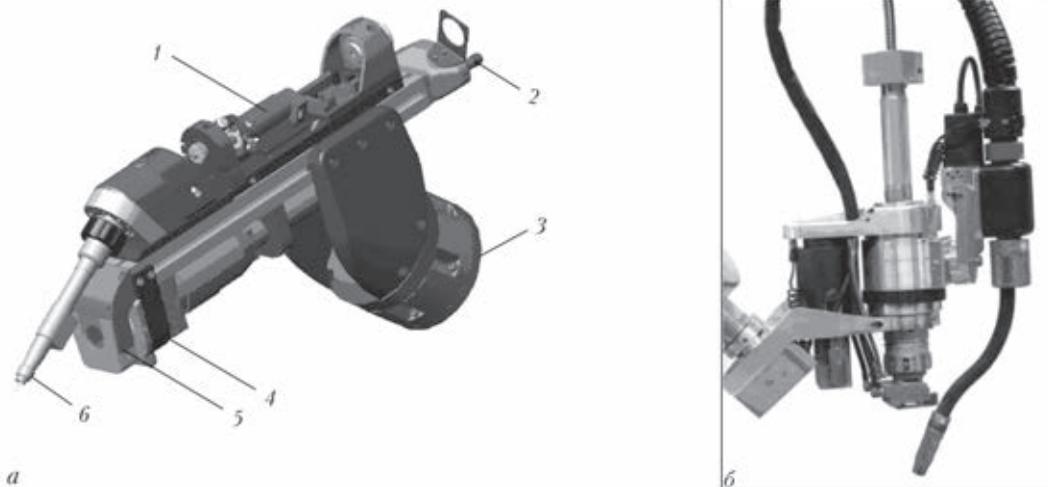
Головки для гибридной лазерно-дуговой роботизированной сварки фирм «Fronius» (а) и «Cloos» (б) [4]: 1 — устройство подачи проволоки; 2 — забор воздуха; 3 — фиксация на руке робота; 4 — защитное стекло; 5 — кросс-джет; 6 — водоохлаждаемый мундштук
